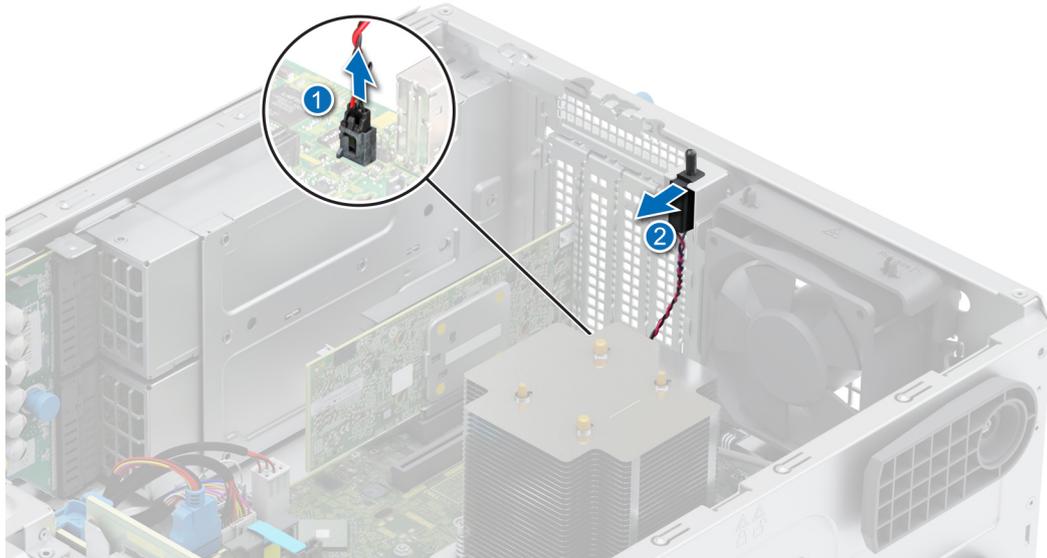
Entfernen des Eingriffsschaltermoduls
